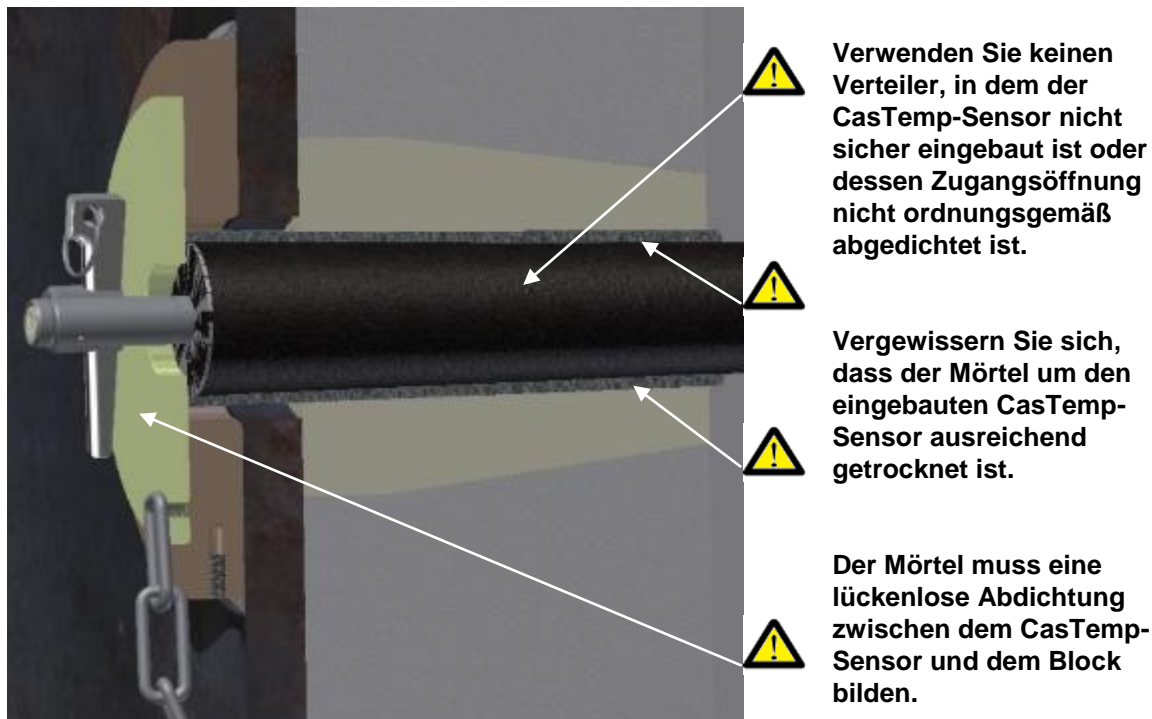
Sobald die Stampfmasse mit dem Block bündig abschließt, können Sie das Einbettwerkzeug entfernen und das formbare feuerfeste Material trocknen.
